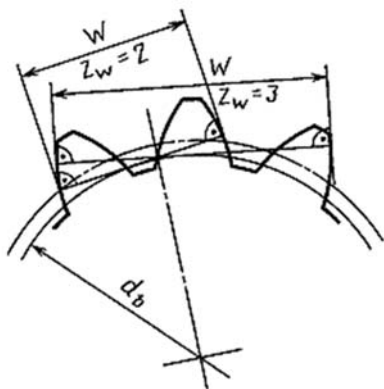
Схема расположения общих нормалей на зубчатом колесе
